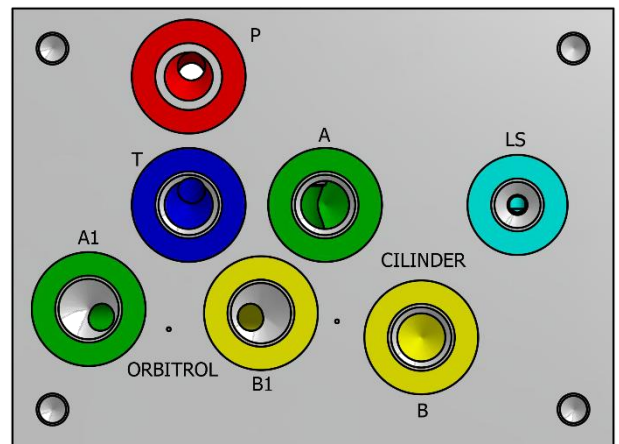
Anschlüsse für das hydraulische Load-Sense Manifold.
